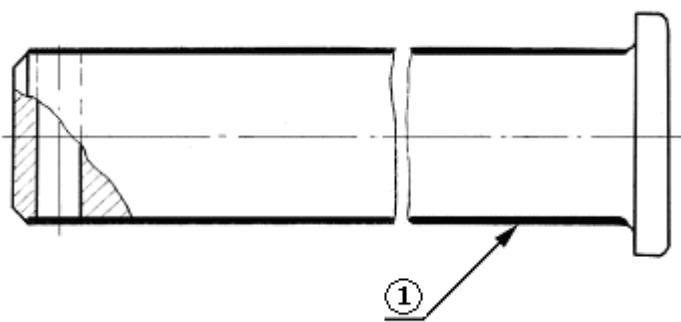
Дефект валика тормозной рычажной передачи, ремонтируемый наплавкой
